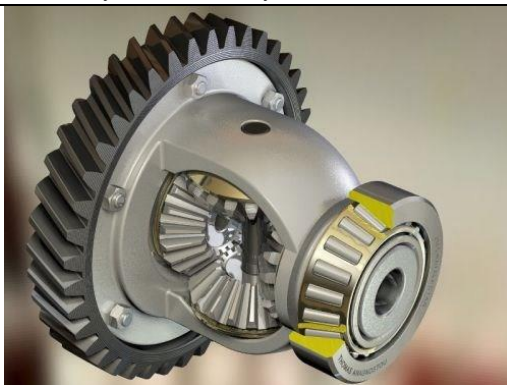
Конструкция дифференциала в чашке в сборе с подшипниками и ведомой цилиндрической косозубой шестерни
